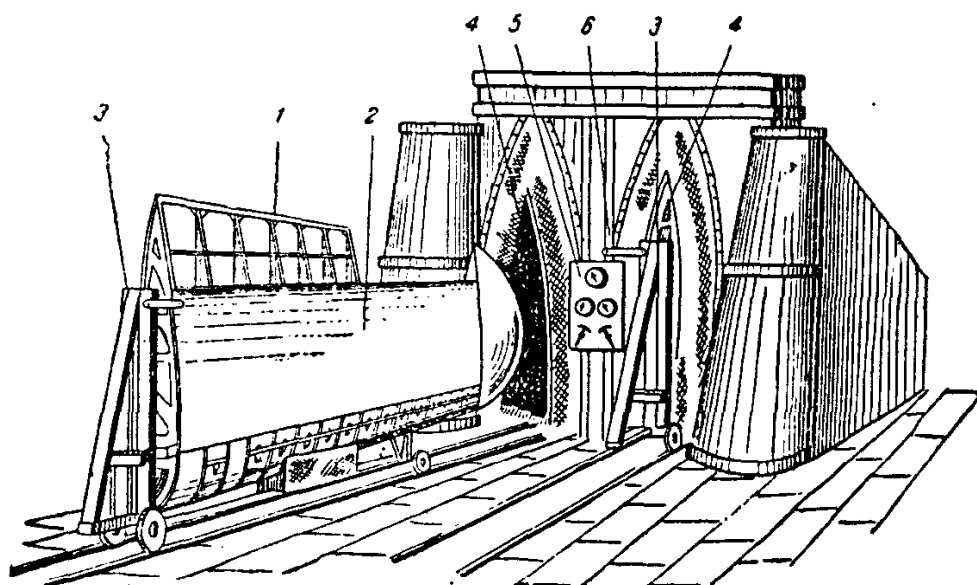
Часть приспособления для малковки каркаса консоли крыла по направляющим.
